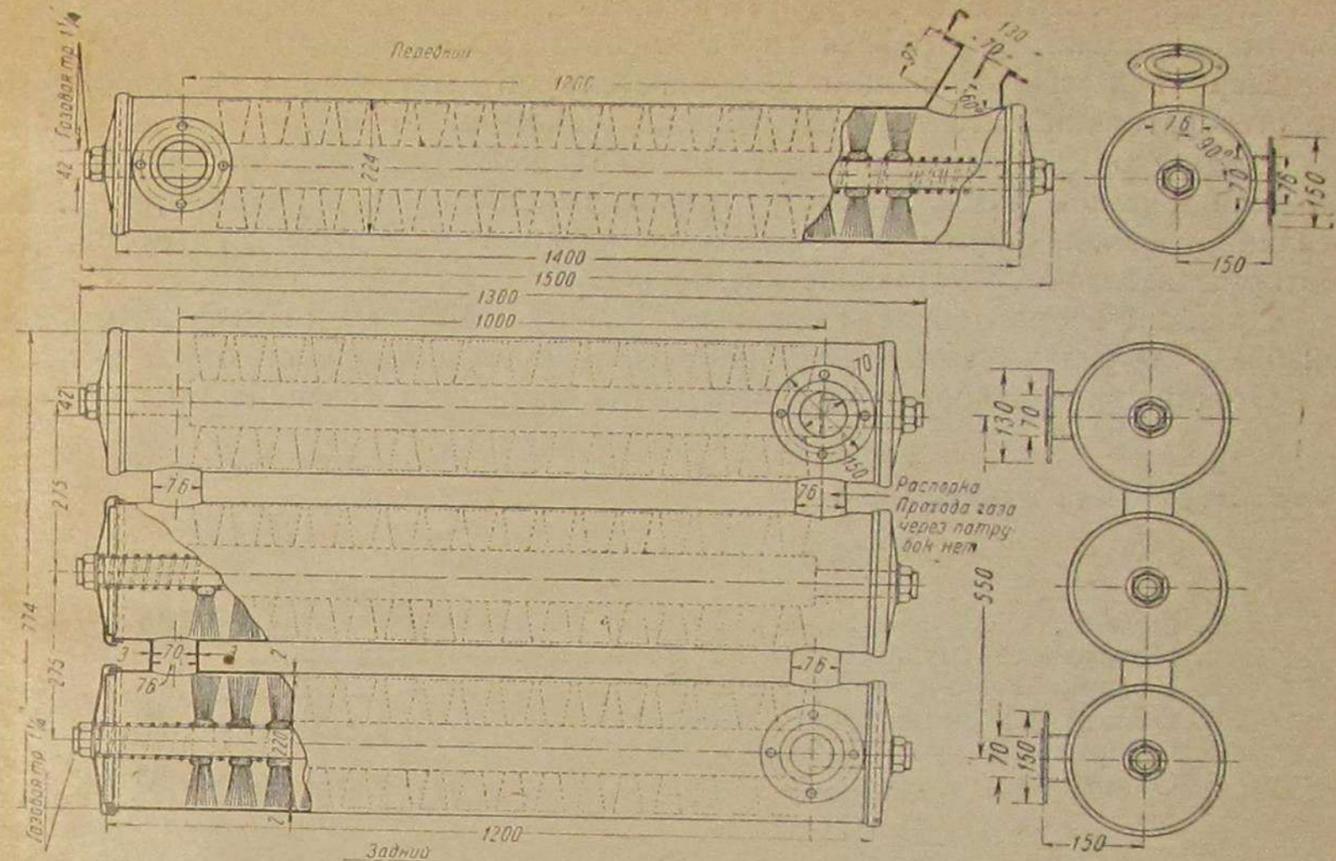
Поверхностный газоочиститель установки „Пионер“ Д-8.
